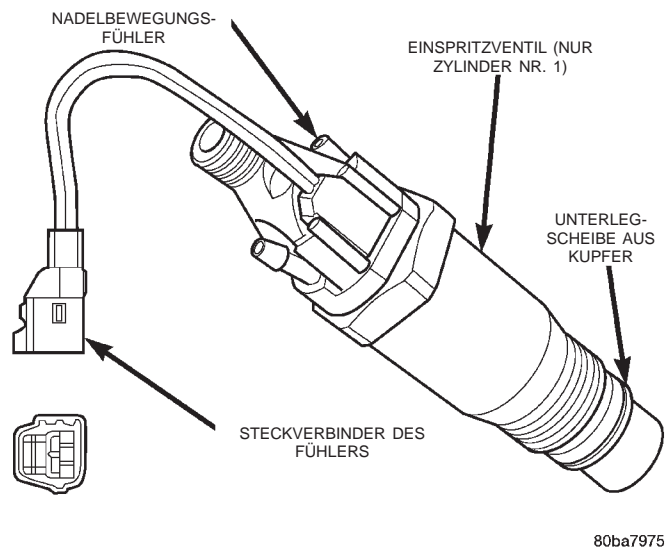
Einspritzventilfühler—Zylinder Nr. 1
